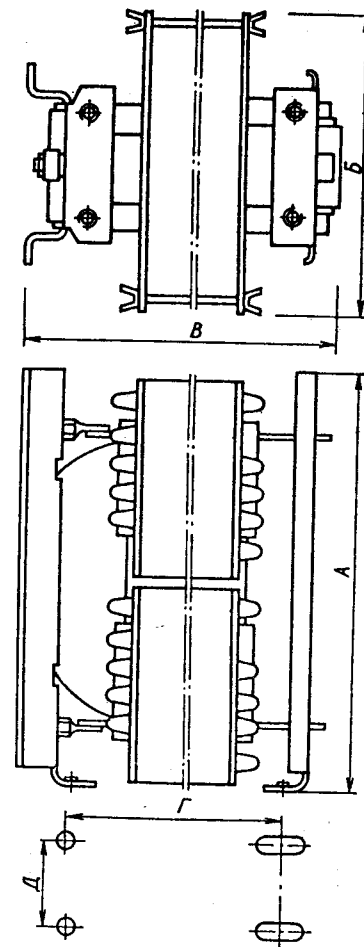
Габаритный чертеж и размеры для крепления силовых трансформаторов
